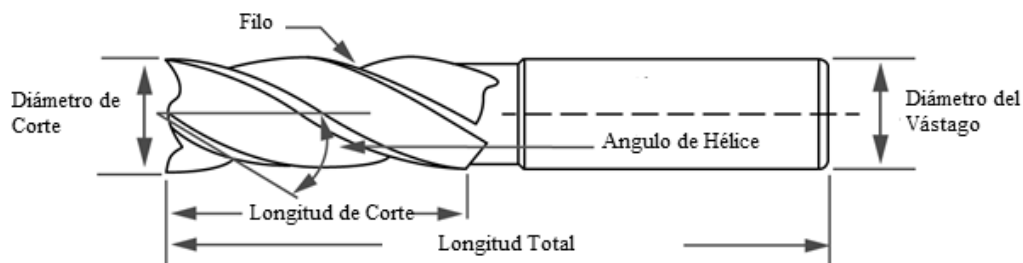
Geometría básica de una herramienta de corte (End Mill)[63].
